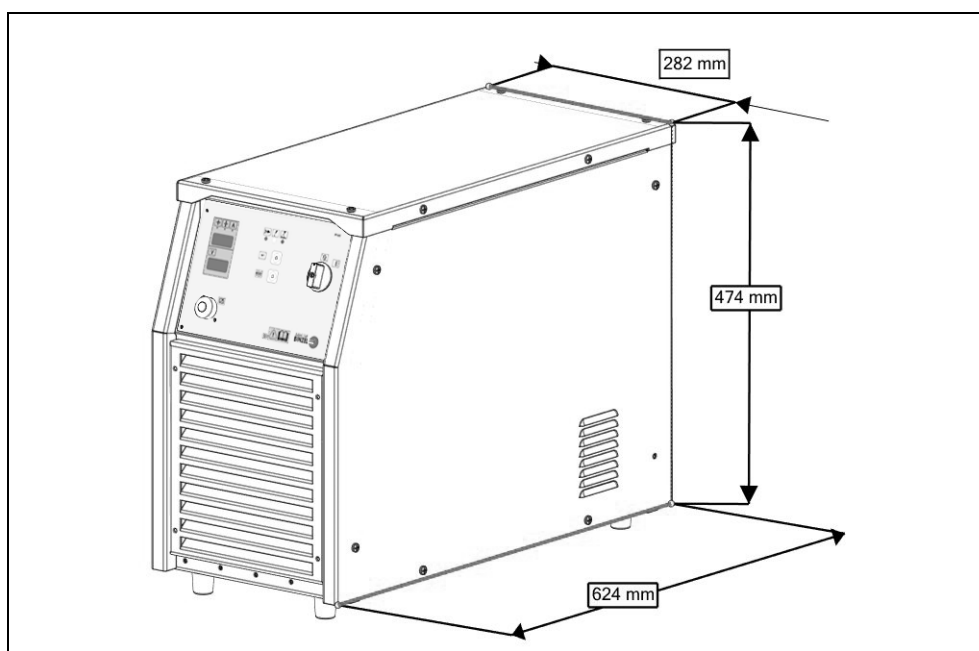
Abmessungen Roboterschweißstromquelle iROB Pulse
